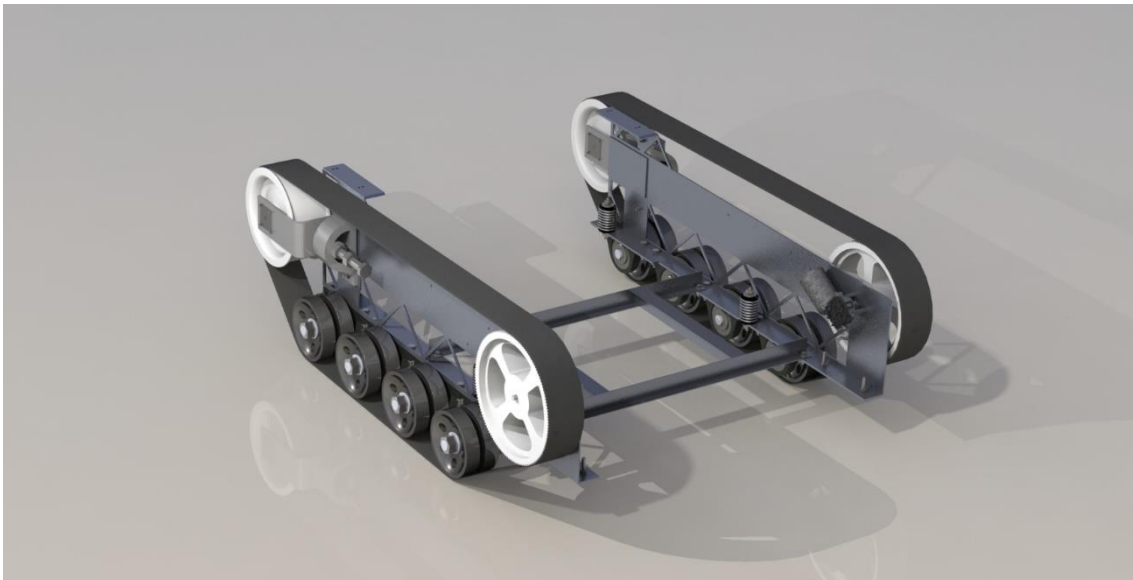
Primer paso en el montaje (sistema de tracción).
